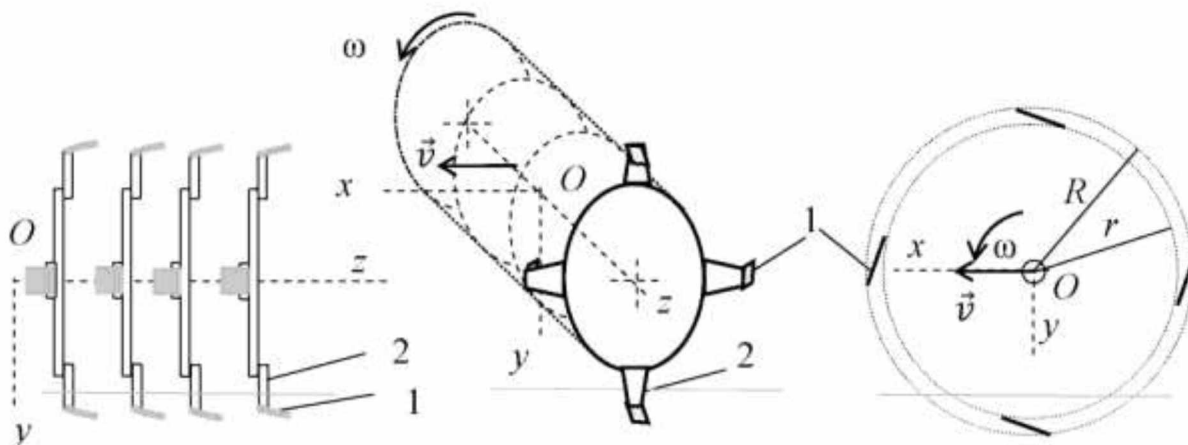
Барабан фрези з ножами 1 і боковинами з ріжучими крайками 2
